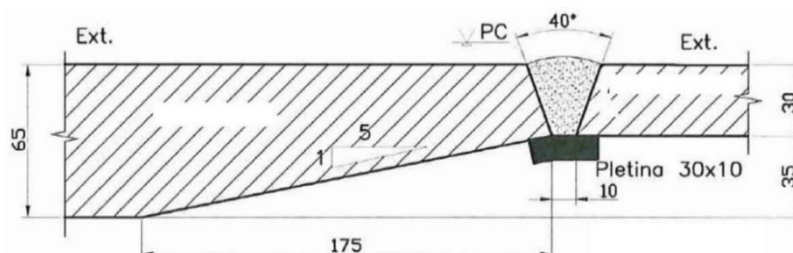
Chapa de respaldo plegada en soldadura de chapas con diferente espesor
